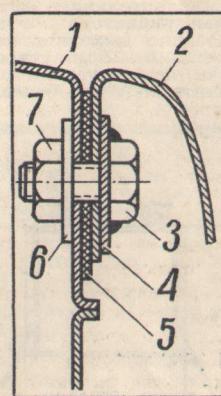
Предлагаемое крепление крыла: 1 — кузов; 2 — крыло; 3 — болт М8; 4 — полосовое железо; 5 — прокладка; 6 — шайба; 7 — гайка.
